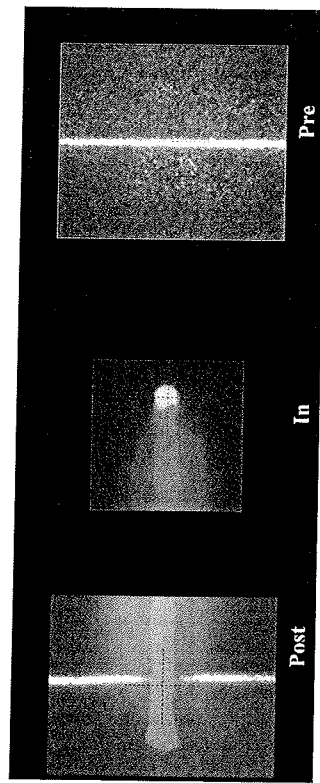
Schweißen eines Testbauteils (Messung S083, Bild-Nr. 11, Vorschub 3 m/min).
